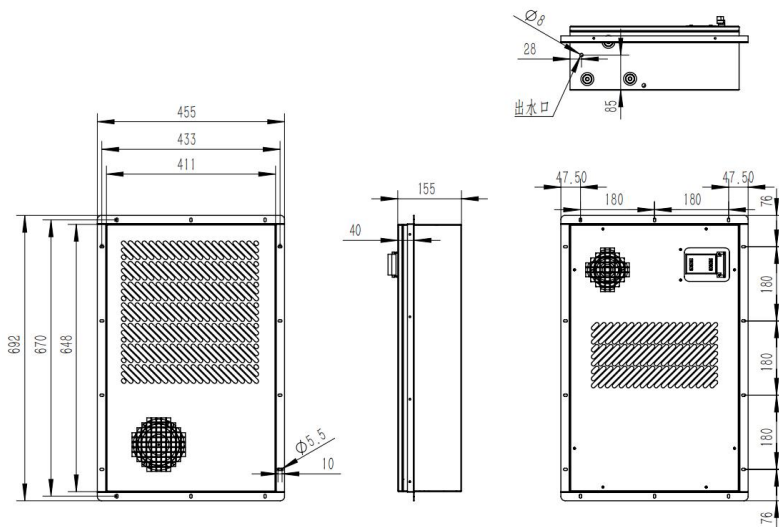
Габаритные размеры SNR-ACC-800-ACH
